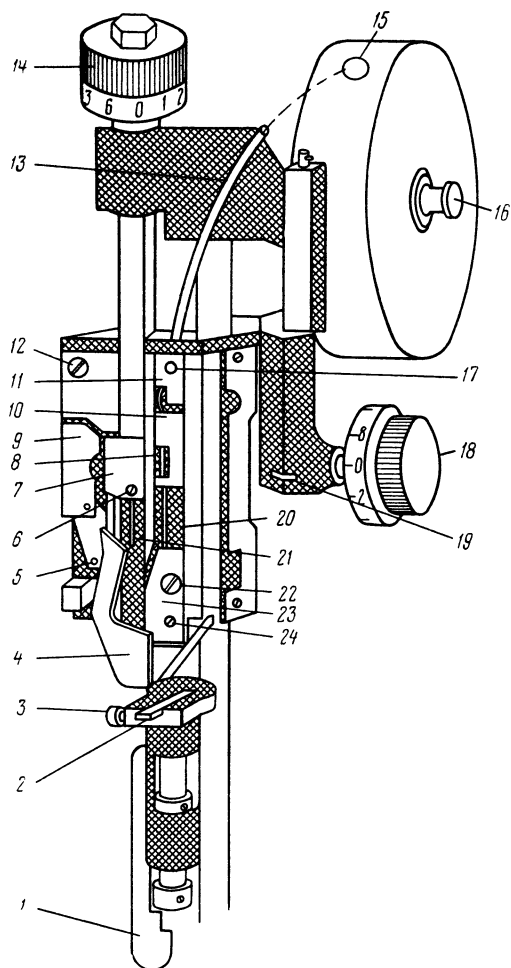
Машина для изготовления и вставки металлических крепителей (модель А):
